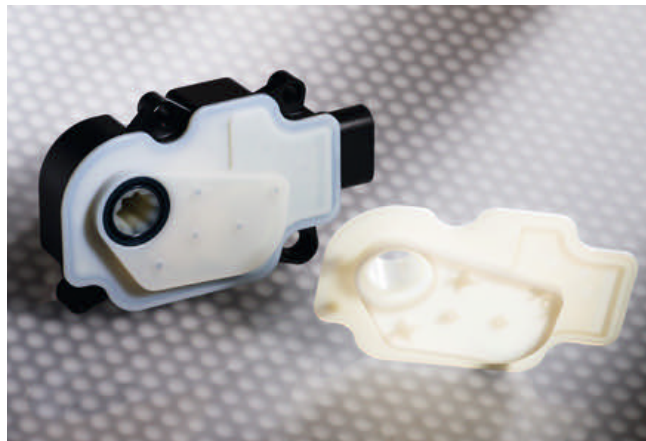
Dank seiner hohen Transparenz für Infrarotlicht lässt sich glasfaserverstärktes Ultradur LUX B4300 G4 sehr schnell und wirtschaftlich im Laserschweißverfahren fügen. Das Material ist bereits in einem Luftklappensteuerungs-Modul von Precision Motors Deutsche Minebea im Serieinsatz
